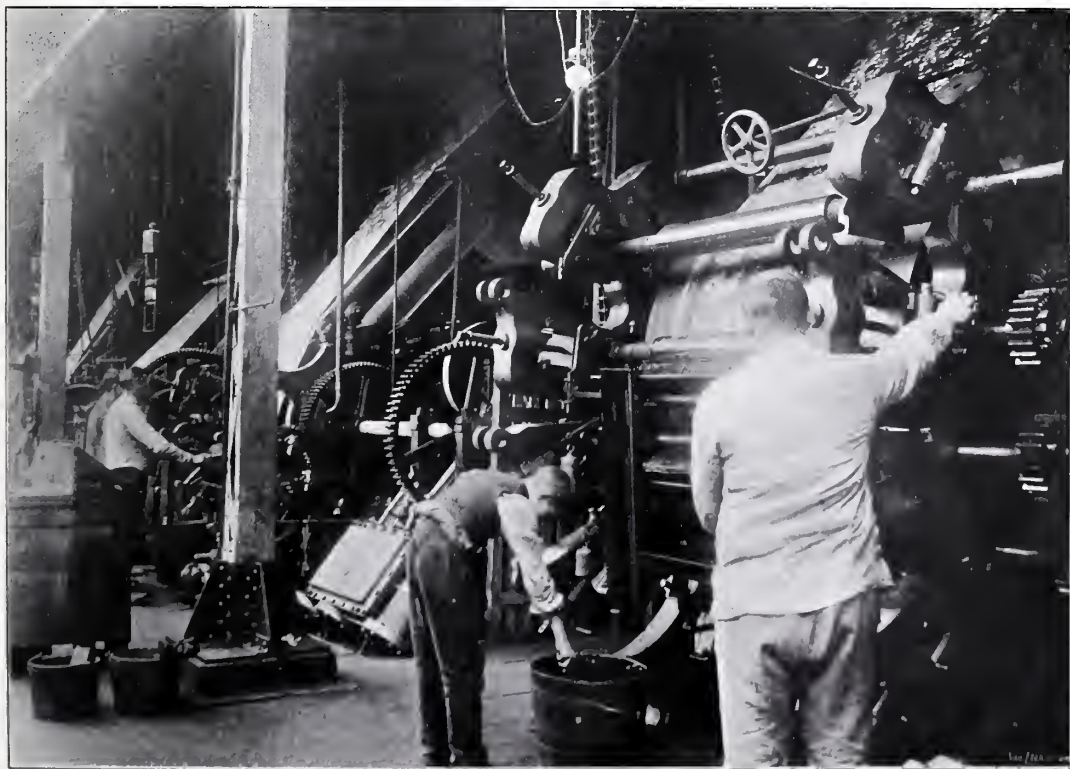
RIJKJE IN DE MACHINALE DRUKKERIJ. DRUKMACHINE.
